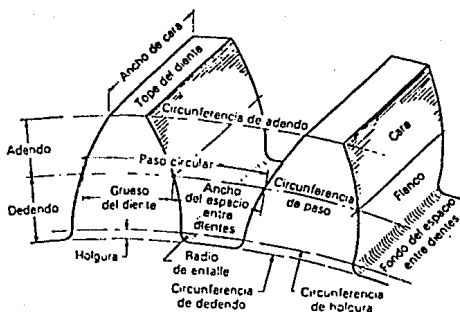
D-9 NOMENCLATURA DEL DIENTE DE ENGRANAJE
